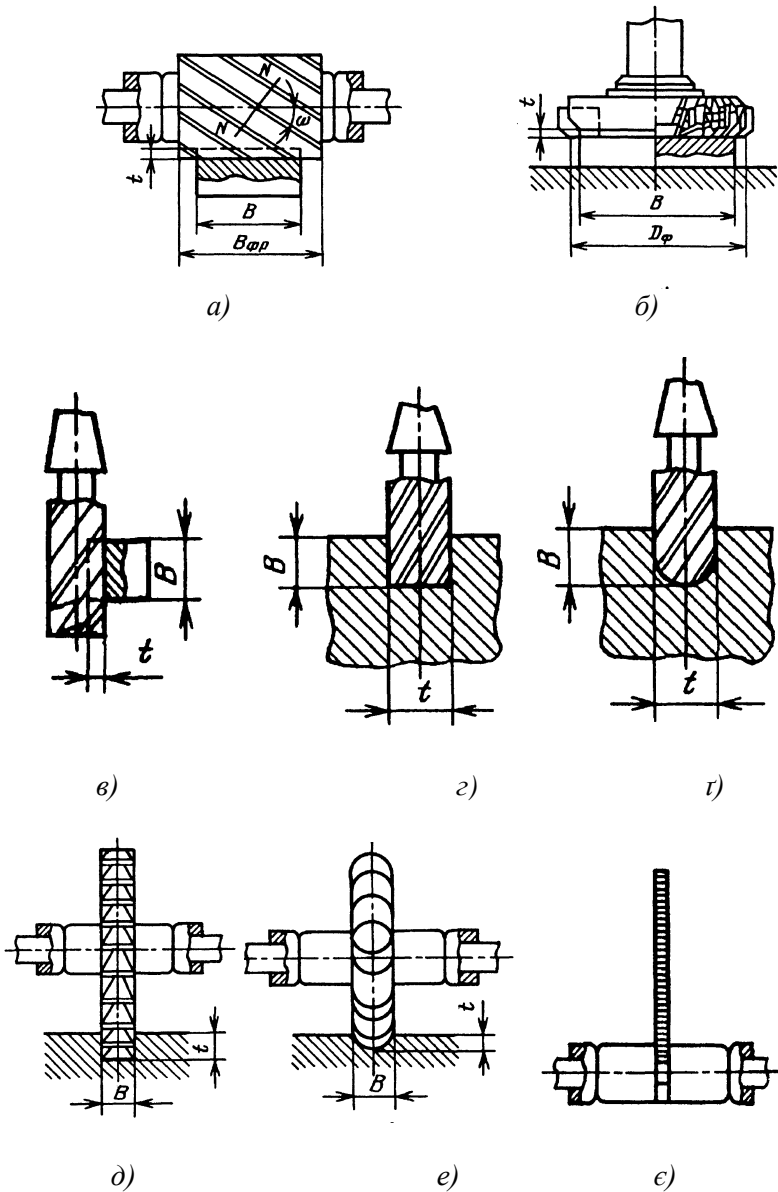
Схеми фрезерування та основні види фрез:
